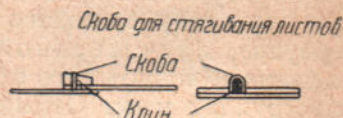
Скоба для стягивания листов при сварке днища
